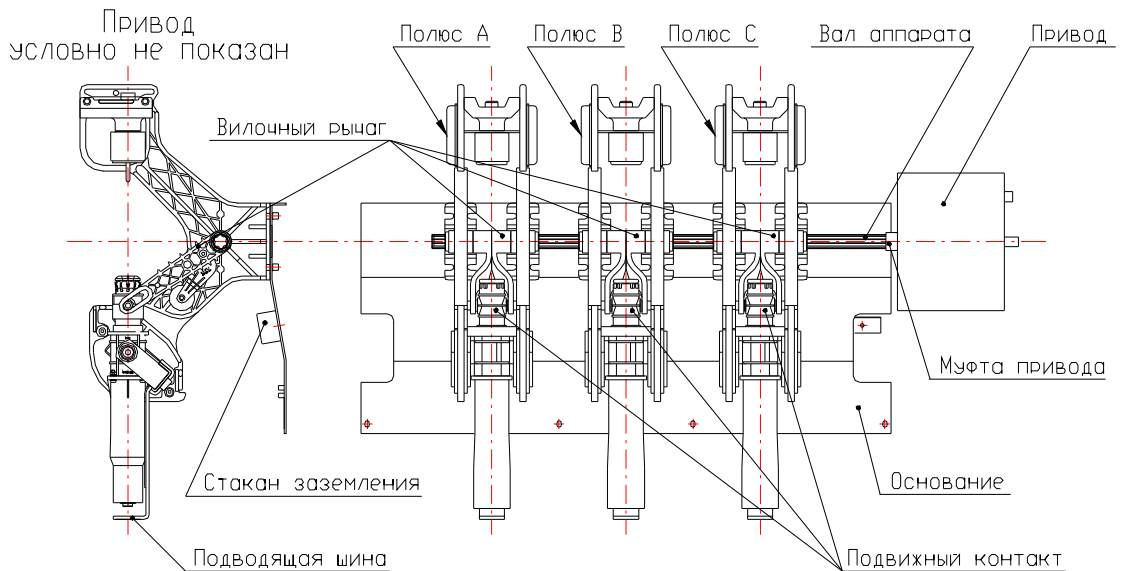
Общий вид выключателя нагрузки и разъединителя.
